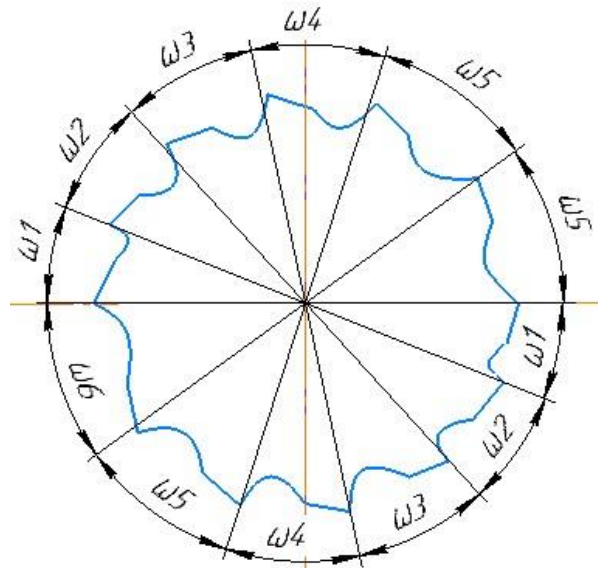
Схема розбивки кроку зубів розвертки
